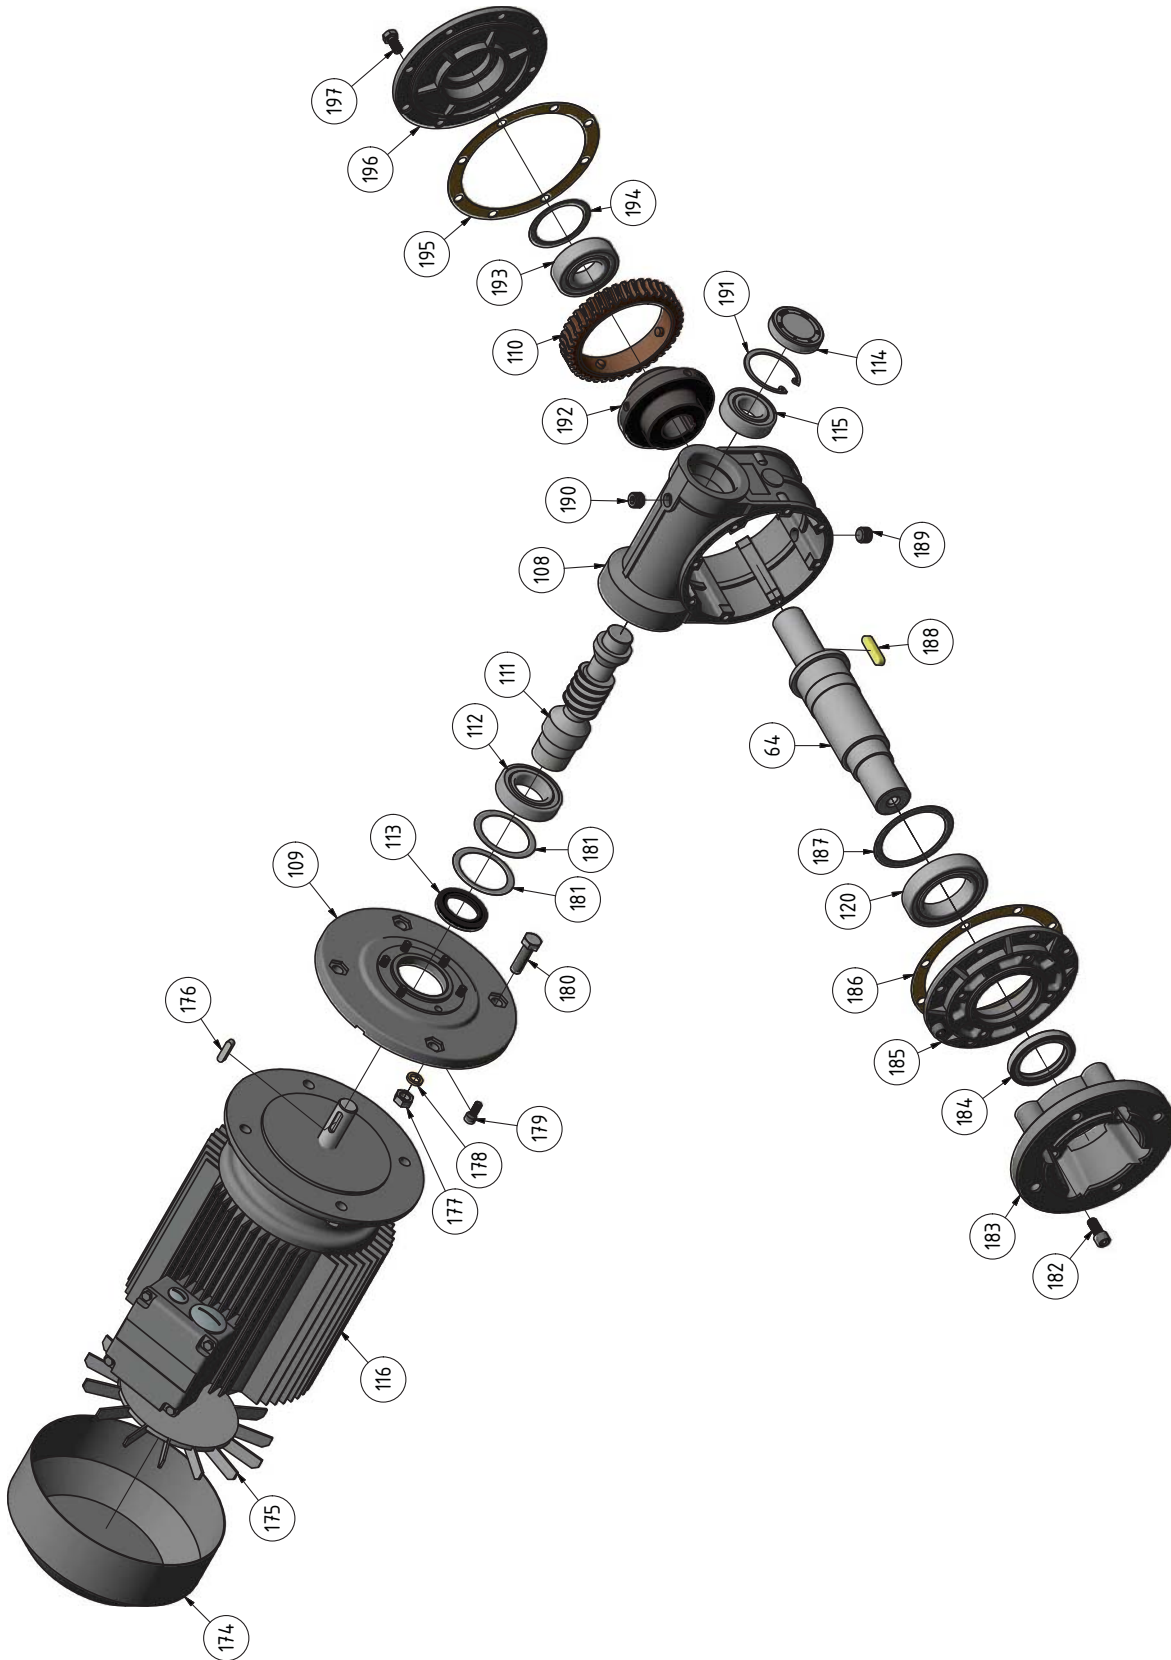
Explosionszeichnung - Drawing spare parts
